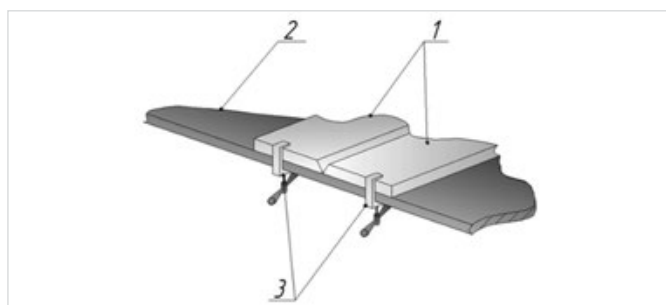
Схема сборки пластин исследований режимов полуавтоматической сварки.
